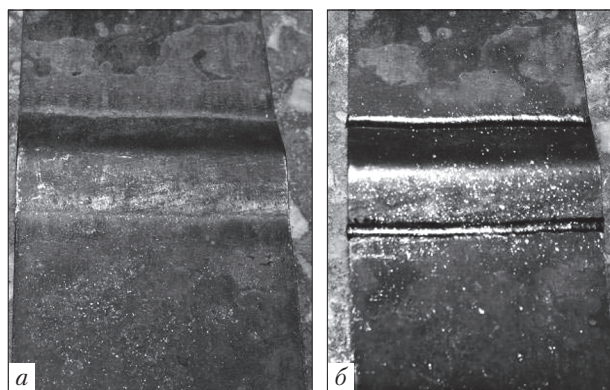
Стиковий зварний шов сталі 09Г2С у вихідному стані після зварювання (а) та після ВМП (б)
